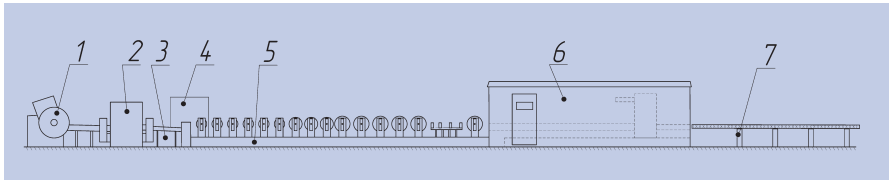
Схема линия профилирования: 1 – ролонная тележка и разматыватель; 2 – правильная машина со столом раскрытия рулона и подачи полосы; 3 – передаточный стол; 4 – шкафы управления; 5 – универсальный стан холодной формовки; 6 – роботизированная система плазменной резки; 7 – выходной рольганг
